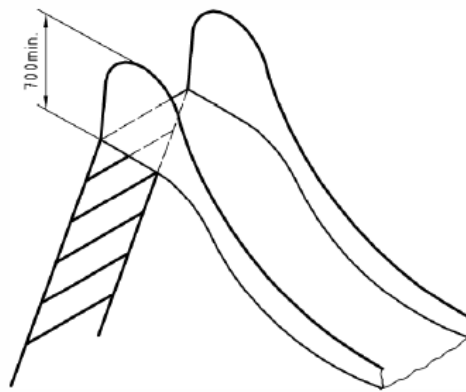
Exemplo de proteção lateral da zona de partida de escorregas isolados. (Dimensões em milímetros)
